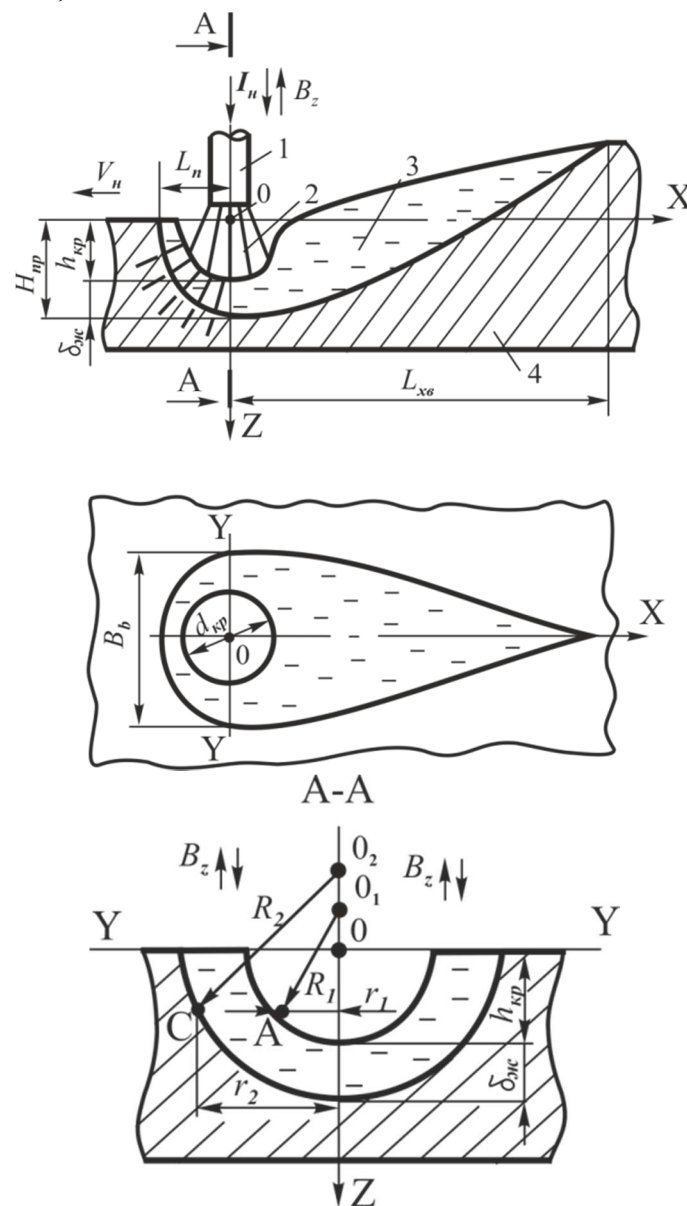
Схема сварочной ванны при дуговой наплавке и ее геометрические размеры:
